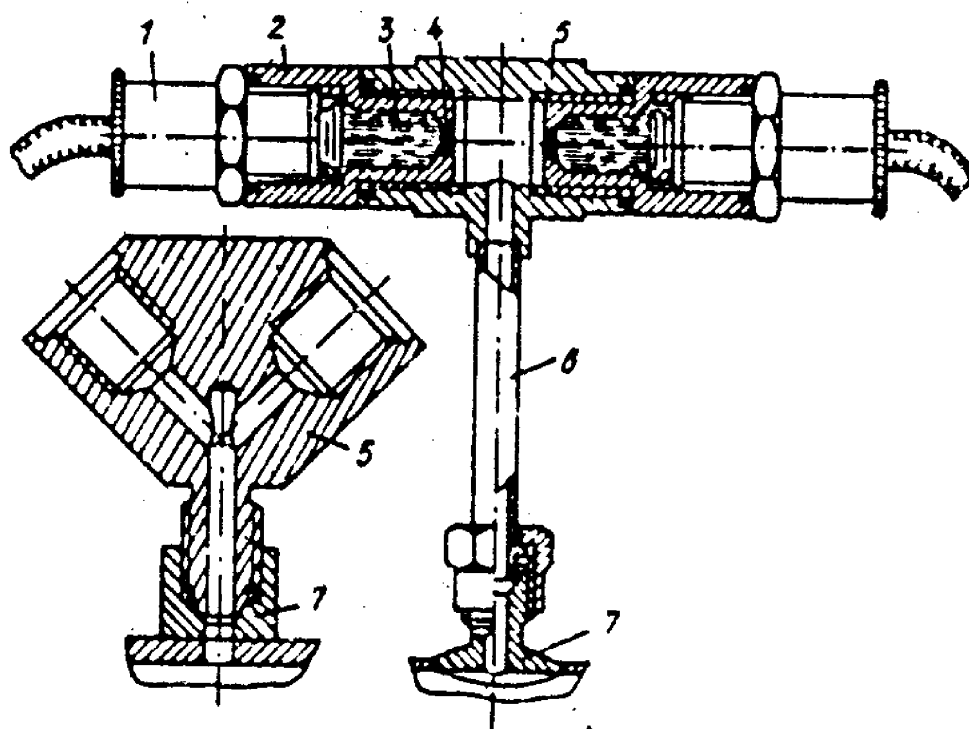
Способы установки датчиков давления на корпусе ДСН:
